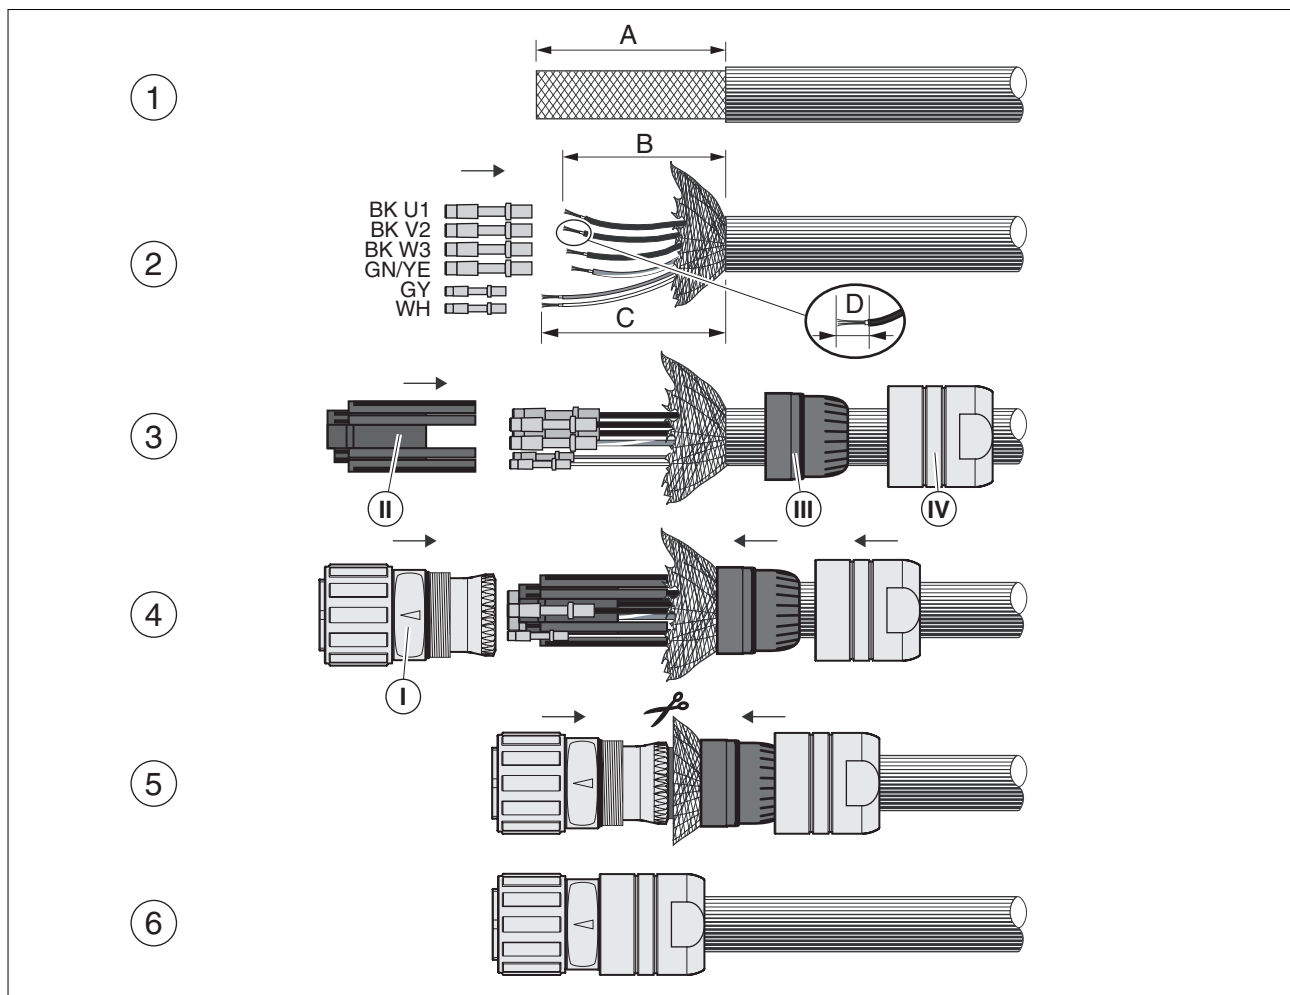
Confeccionar el cable del motor con conector de motor M40
